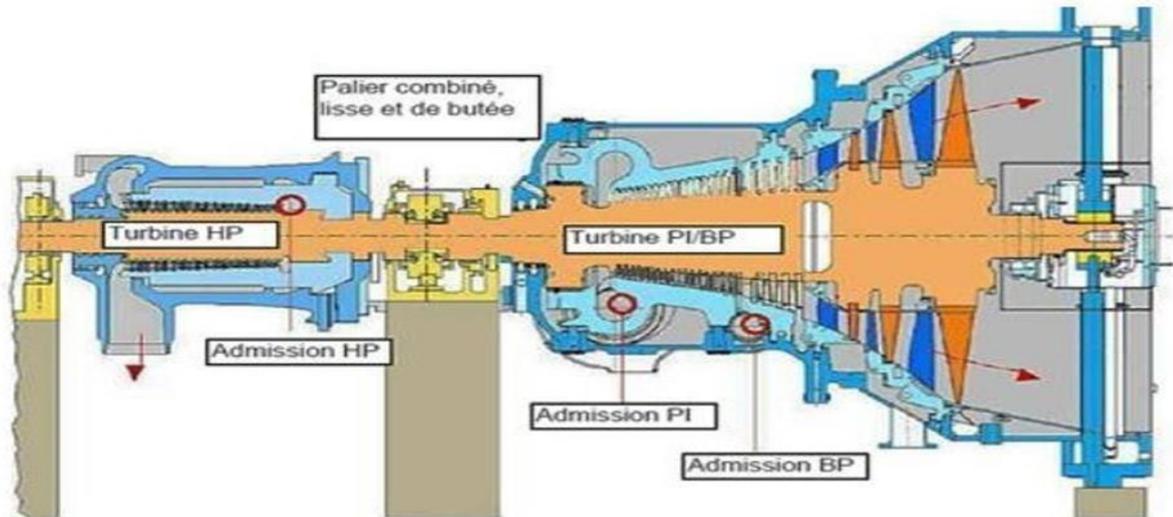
Vue en coupe d'une turbine à vapeur [2]
